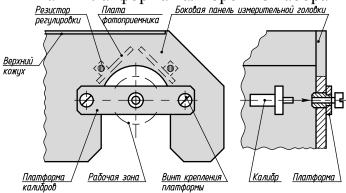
Установка калибра в рабочую зону.
